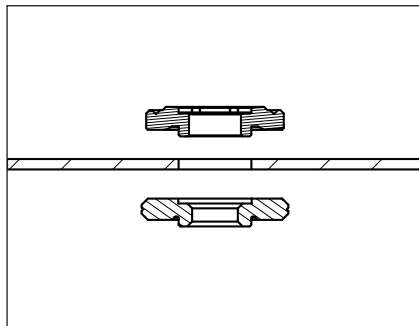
Lato di montaggio del dado di bloccaggio per dischi sottili
